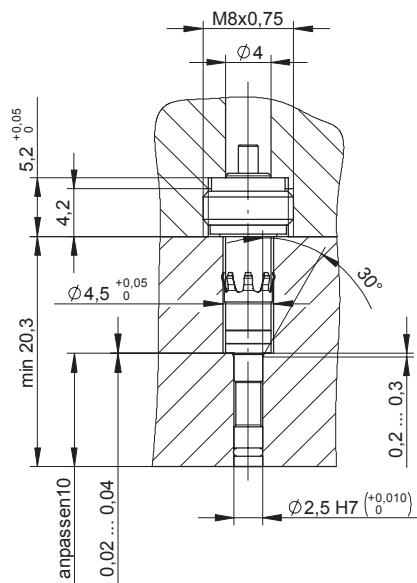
Einbau der Typen 6182C...N... mit ladungsführender Distanzhülse
